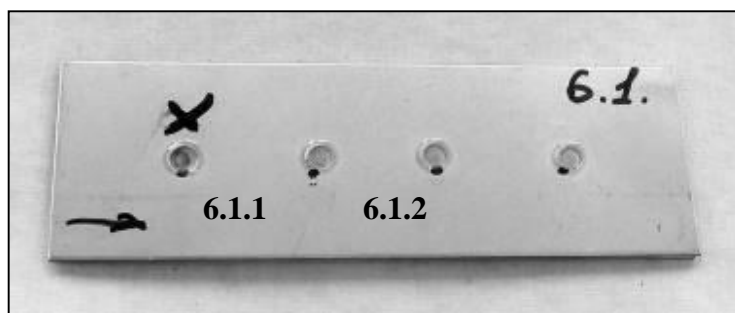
Внешний вид точечной контактной сварки образца № 6.1
